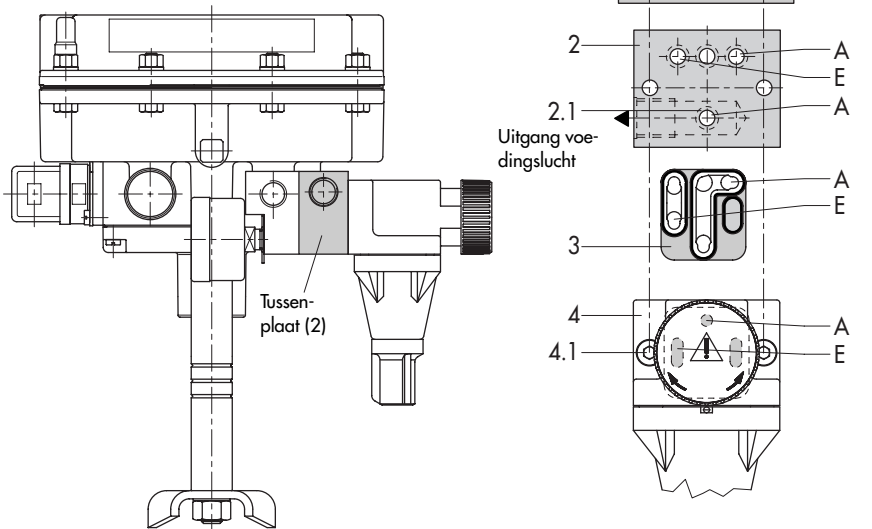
· Montage van een tussenplaat bij aandrijving 3372
